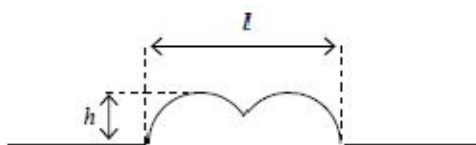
Définitions de la largeur caractéristique des cordons de soudure.
